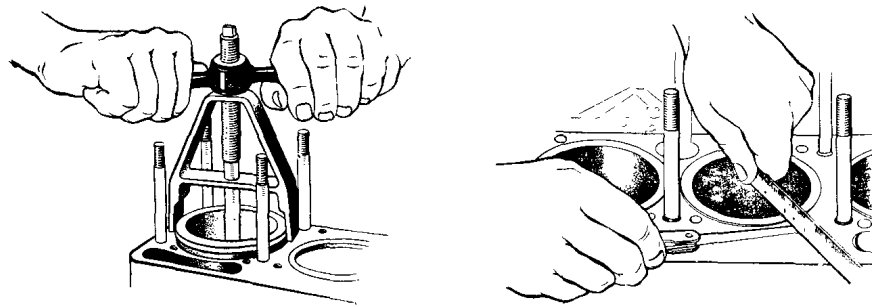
Приспособление для удаления гильз из блока цилиндров
